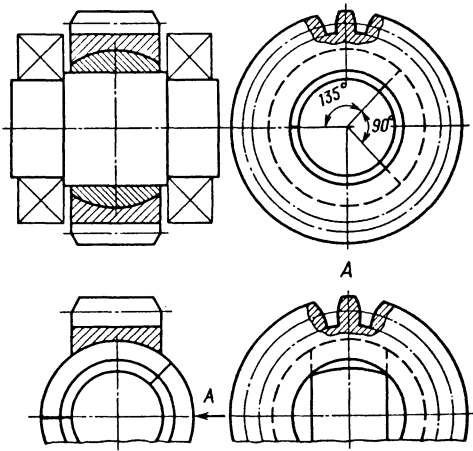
Самоустанавливающийся спутник конструкции В.Н. Ермака
